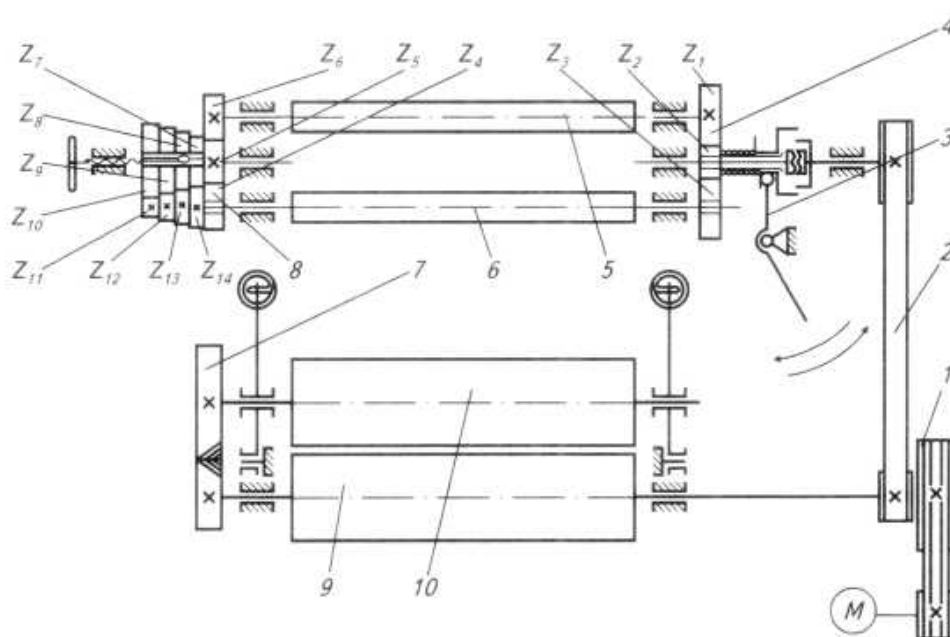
Схема пневмомеханизма управления «привалом» и «отвалом» медленновращающегося вальца станка РМ-4
